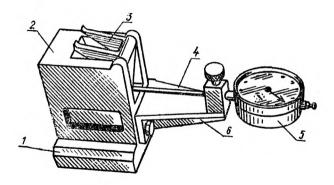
Приспособление для контроля коленчатых валов: 1 — основание приспособления; 2 — упор; 3 — двуплечий рычаг; 4 — удлинитель; 5 — индикатор; 6 — кронштейн для индикатора.
